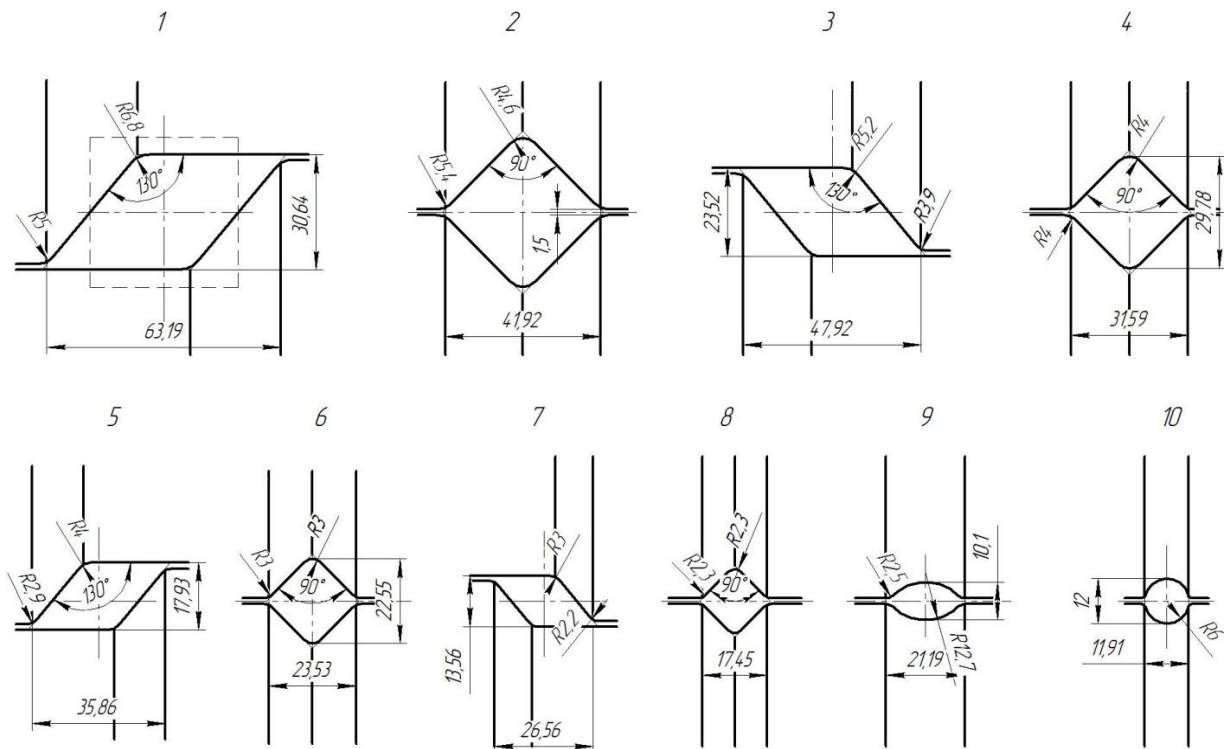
Схема калибровки валков для прокатки катанки на лабораторном полупромышленном стане «ДУО-200/150»
